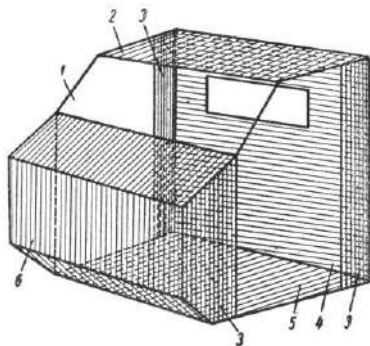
Різні силові схеми несучого корпусу легкового автомобіля
